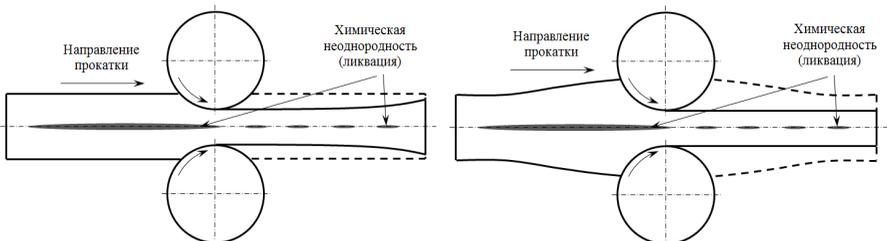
Интенсификация деформационной проработки внутренних слоёв металла: прокатка с изменяющимся зазором между валками (а) и прокатка непрерывнолитой заготовки с выпуклой формой поперечного сечения (б)
